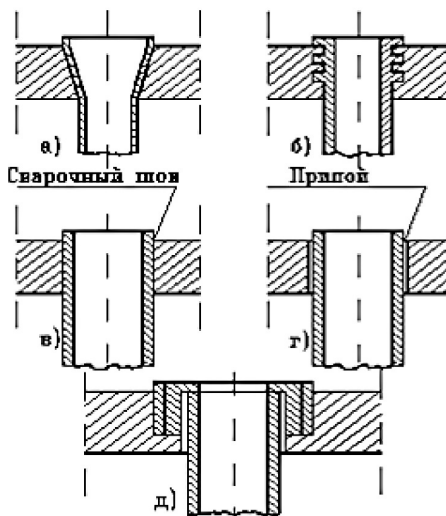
Закрепление труб в трубных решетках: а — развальцовкой; б — развальцовкой с канавками; в — сваркой; г — пайкой; д — сальниковыми устройствами
